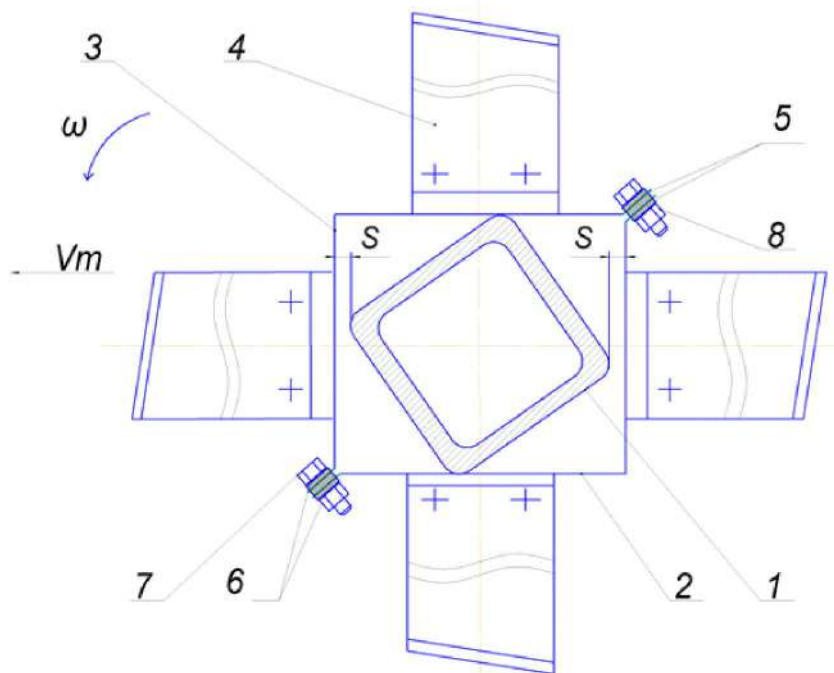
Конструкция № 2 предохранительного устройства для секции почвообрабатывающей фрезы.
